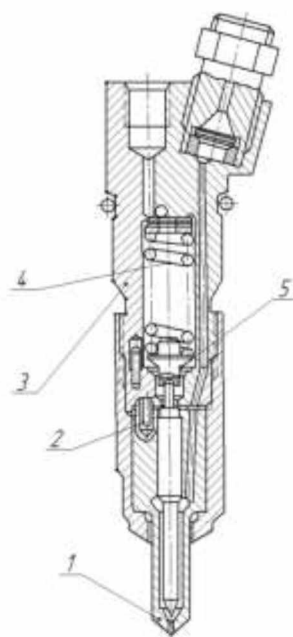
Форсунка КАМАЗ -740: 1 – розпилювач; 2 – інсталяційний штифт; 3 – корпус форсунки; 4 – пружина; 5 – шайба упорна
